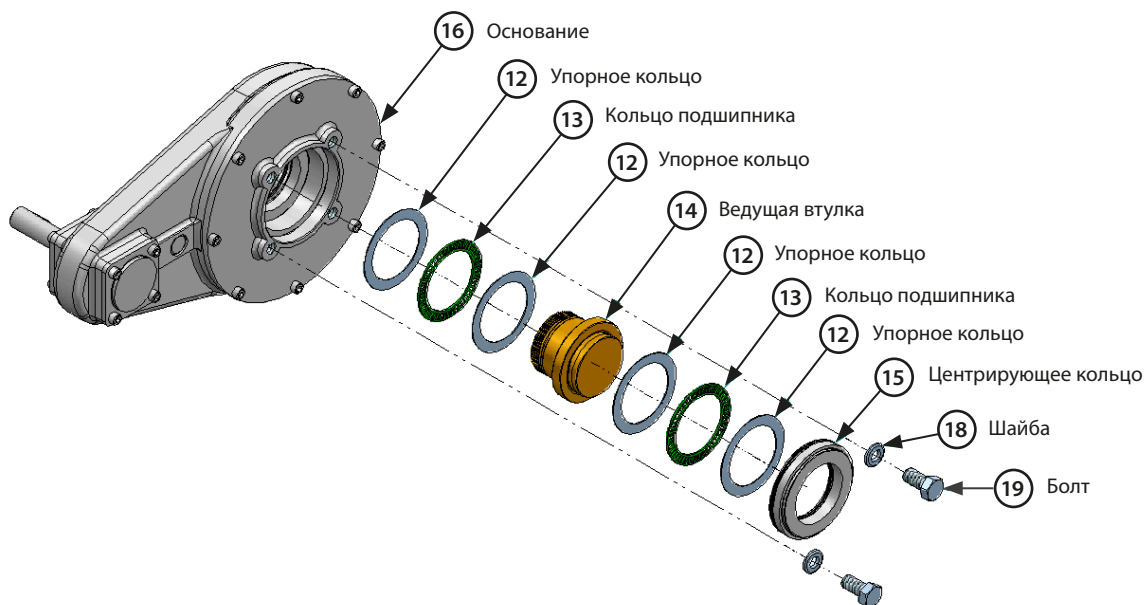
Ведущая втулка конического и цилиндрического редуктора в сборе
